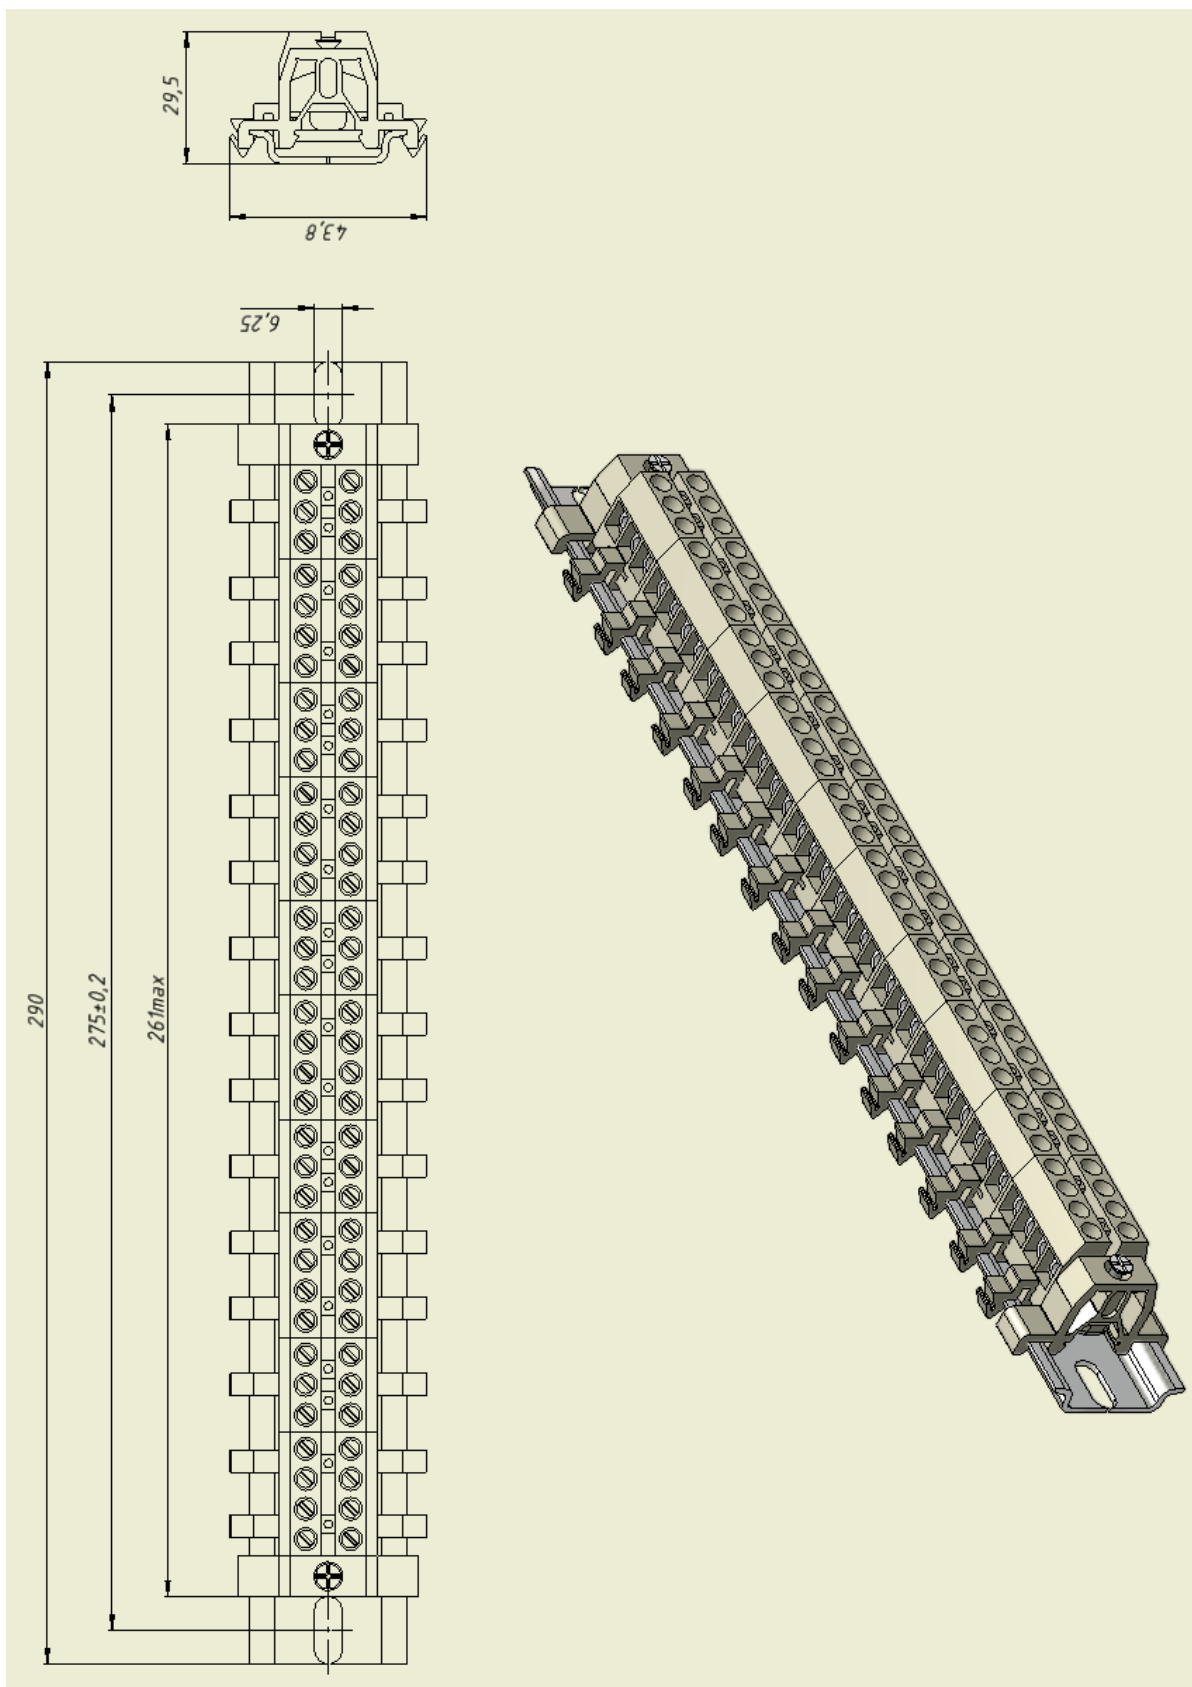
Габаритные размеры DIN-рейки с клеммниками
